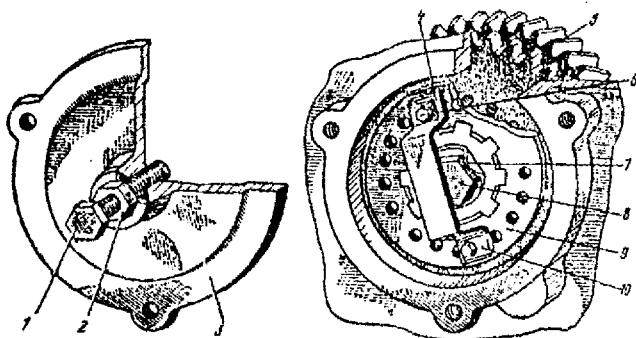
Привод топливного насоса УТН-5 (Д-240): 1 – регулировочный болт; 2 – контргайка; 3 – крышка люка; 4 – планка; 5 – шестерня привода топливного насоса и компрессора; 6 – болт; 7 – стопорная шайба; 8 – гайка; 9 – шлицевый фланец шестерни насоса; 10 – замковая шайба
